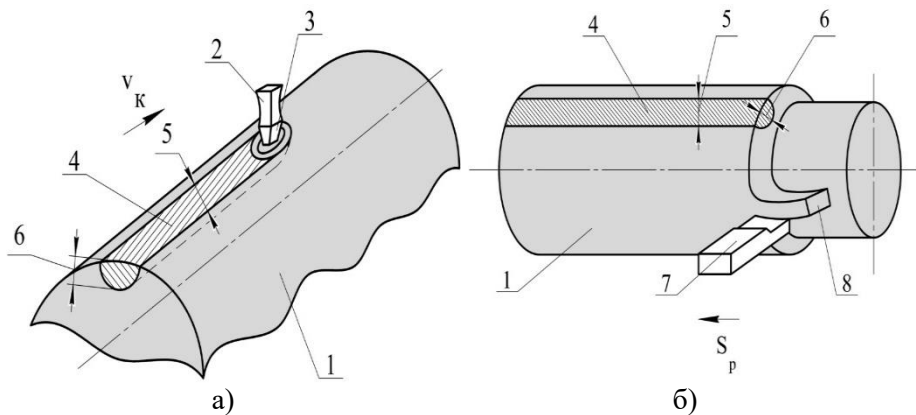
Метод механической обработки деталей типа «тел вращения» из сталей аустенитного класса: а) предварительное ЛКВ на поверхности заготовки; б) процесс механической обработки с ЛКВ,
